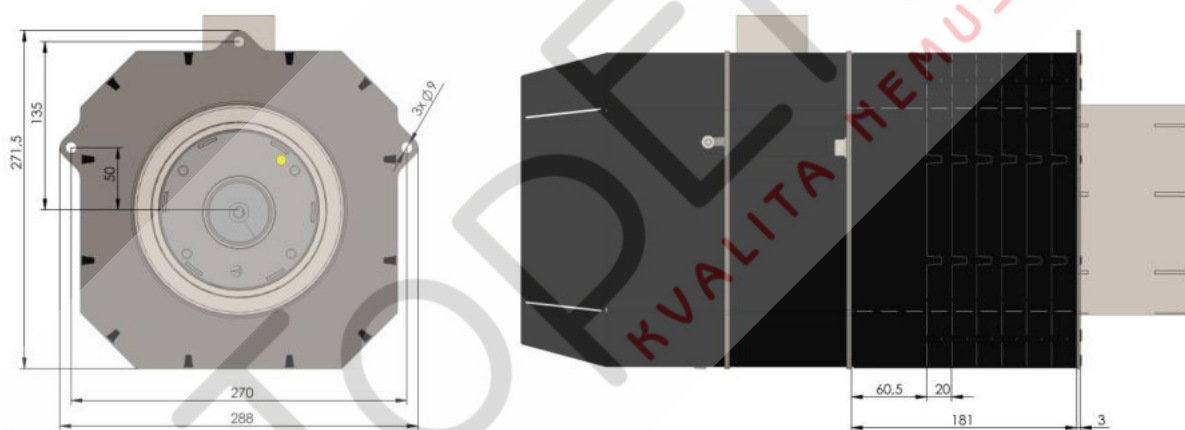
Pohled na hořák 8-36 kW s izolačním pláštěm a montážní deskou.
